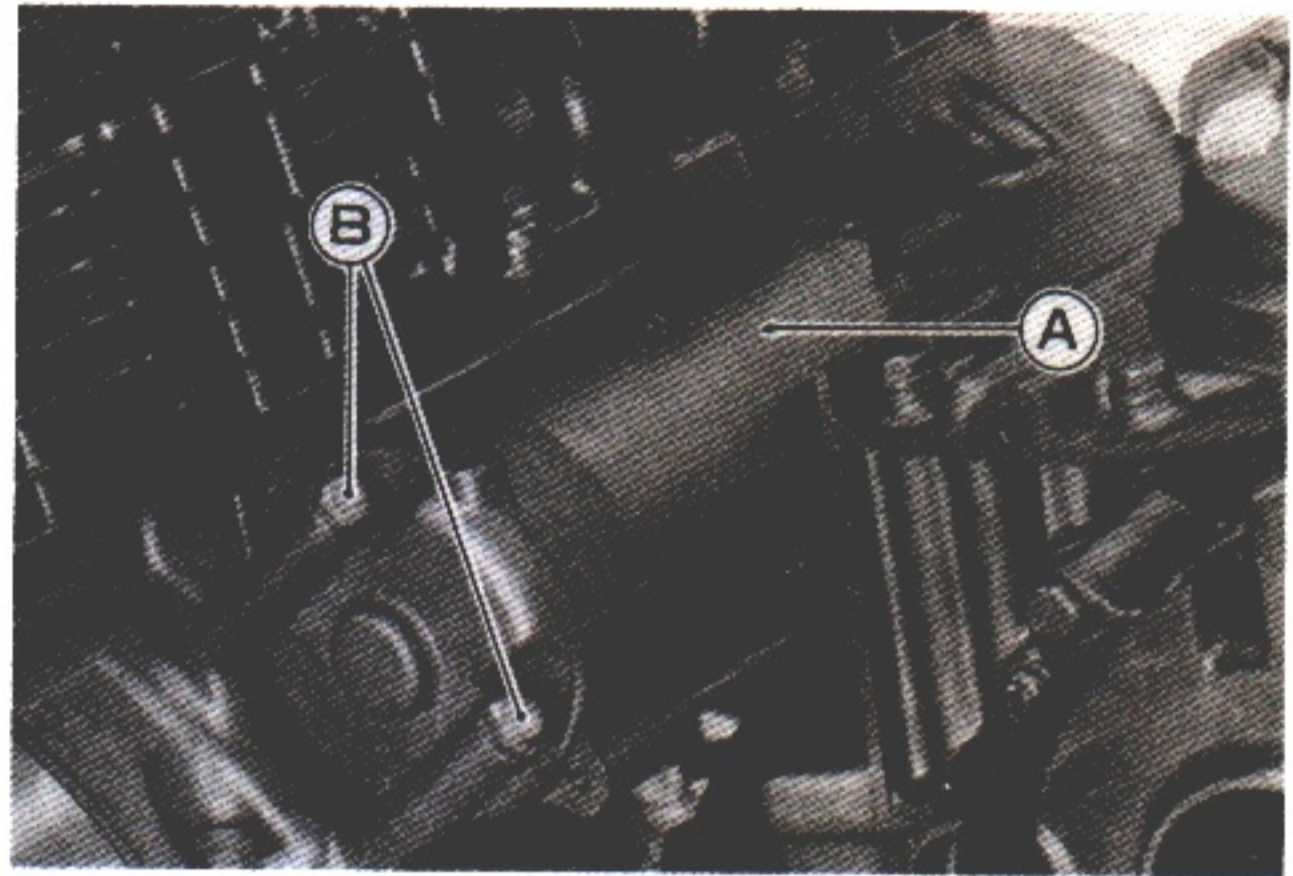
Para desmontar el motor de arranque de la moto hay que sacar los tornillos B que lo sujetan en su posición. A, motor de arranque.
